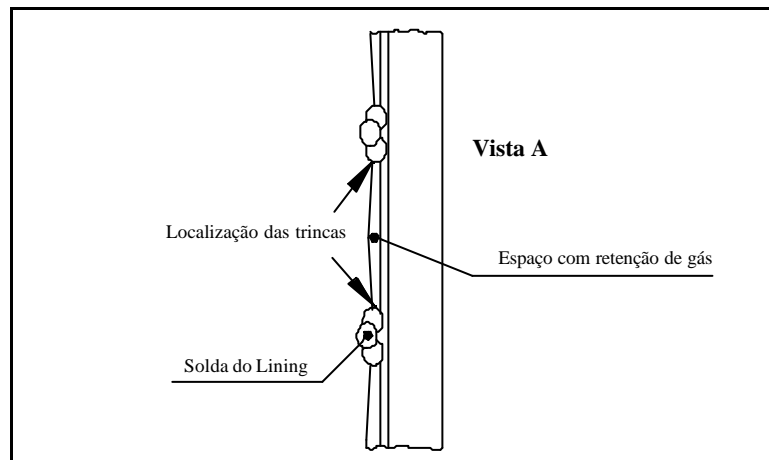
Representação do detalhe da soldagem do *lining*.
